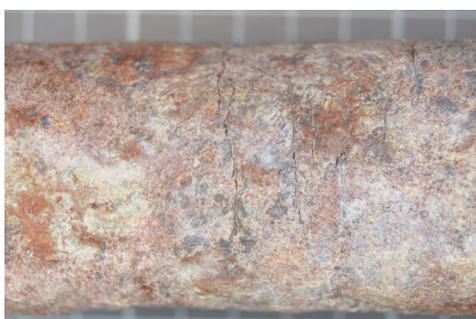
Detalle de las grietas transversales a lo largo de la tubería.
